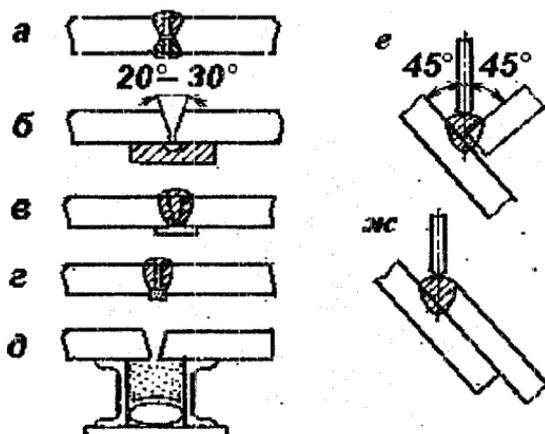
Формування шва за автоматичного зварювання: а – двобічний шов; б – на мідній підкладці, що вилучається; в – на підкладці, яка залишається; г – з ручним підварюванням кореня шва; д – на флюсовій подушці; е і ж – зварювання «у лодочку».
